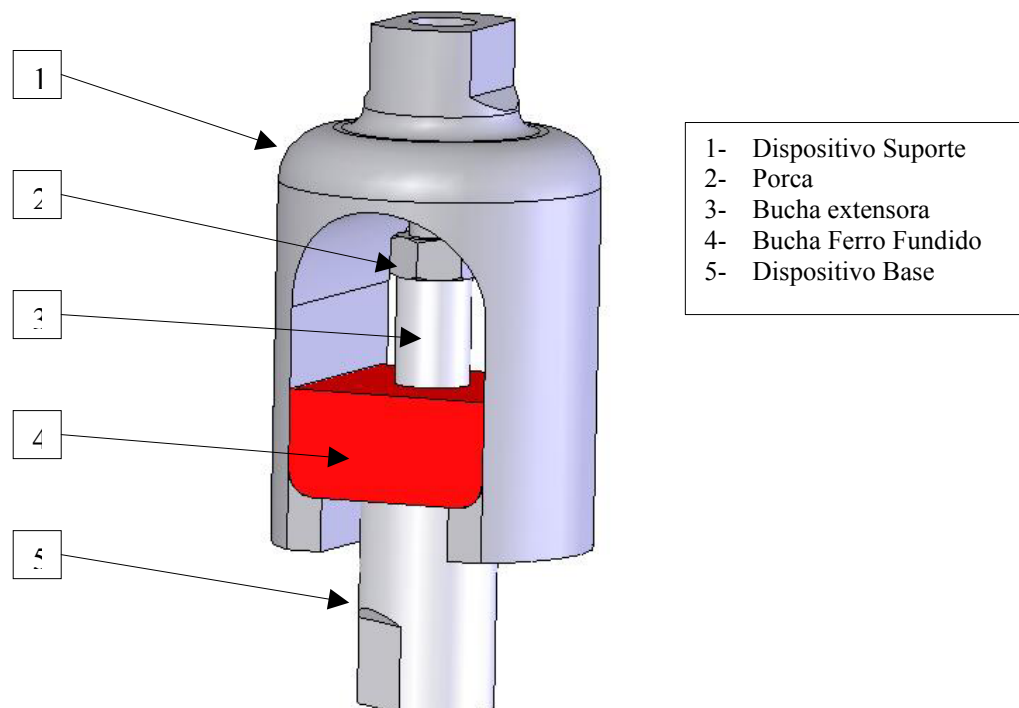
Ilustração da montagem do dispositivo para ensaio de fadiga no atuador de 250kN.
